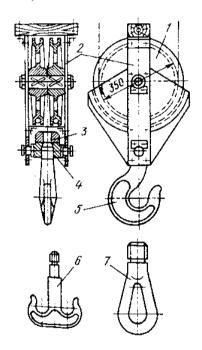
Крюковая обойма подвижных блоков и грузозахватные приспособления: 1 – подвижные блоки; 2 – щеки; 3 – гайка; 4 – траверса (поперечина); 5 – однорогий крюк; 6 – двурогий крюк; 7 – грузовая петля
